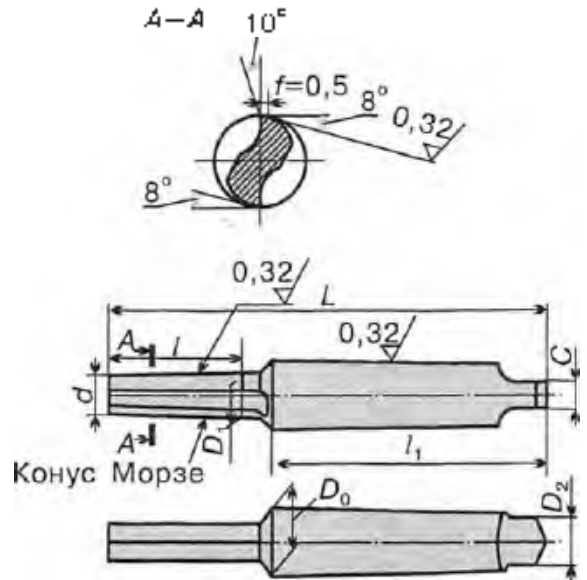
ДВОПЕРОВИЙ КІНЦІЙНИЙ ЗЕНКЕР (НІЖ) ДЛЯ ОБРОБКИ СТАНДАРТНИХ КОНУСІВ МОРЗЕ
